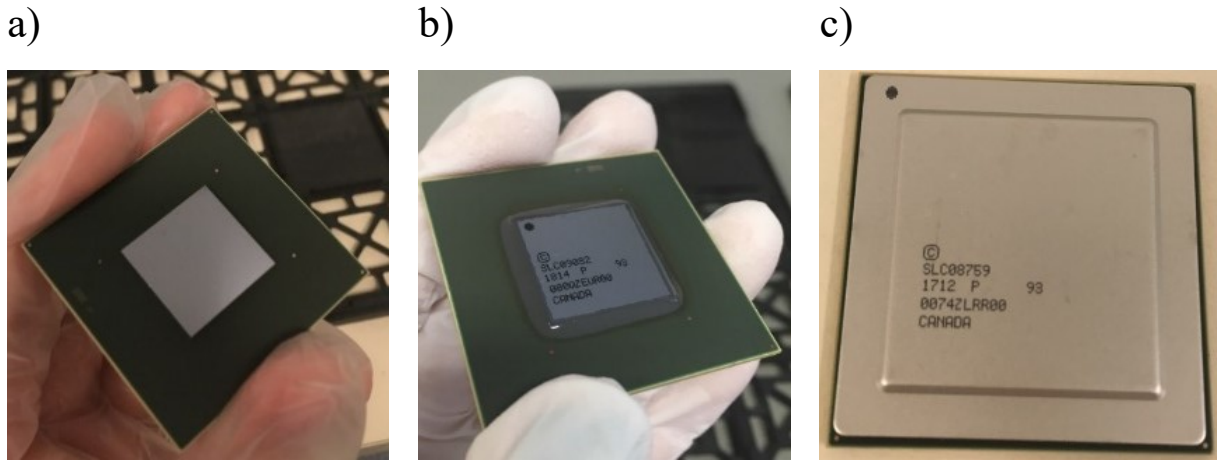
Photographie du a) Module assemblé sans matériau de remplissage b) Module assemblé avec matériau de remplissage c) Module assemblé avec matériau de remplissage et capot [17].
